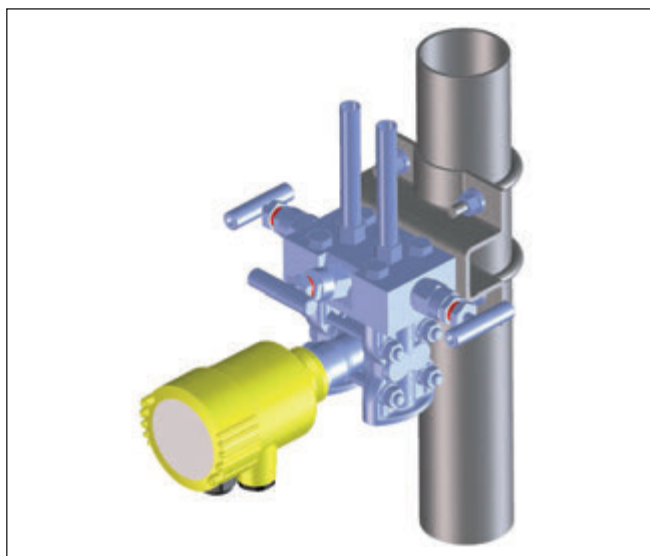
Пример монтажа: универсальный держатель для вентильного блока
